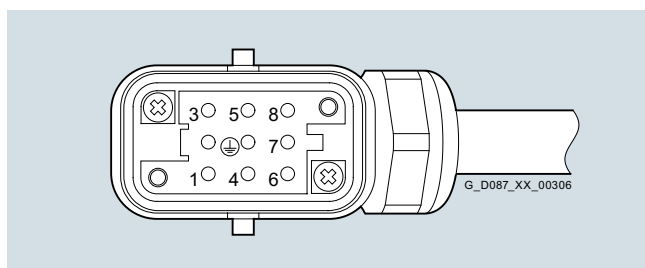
/28 Pinbelegung bei Motorstecker mit Kabel 0,5m
